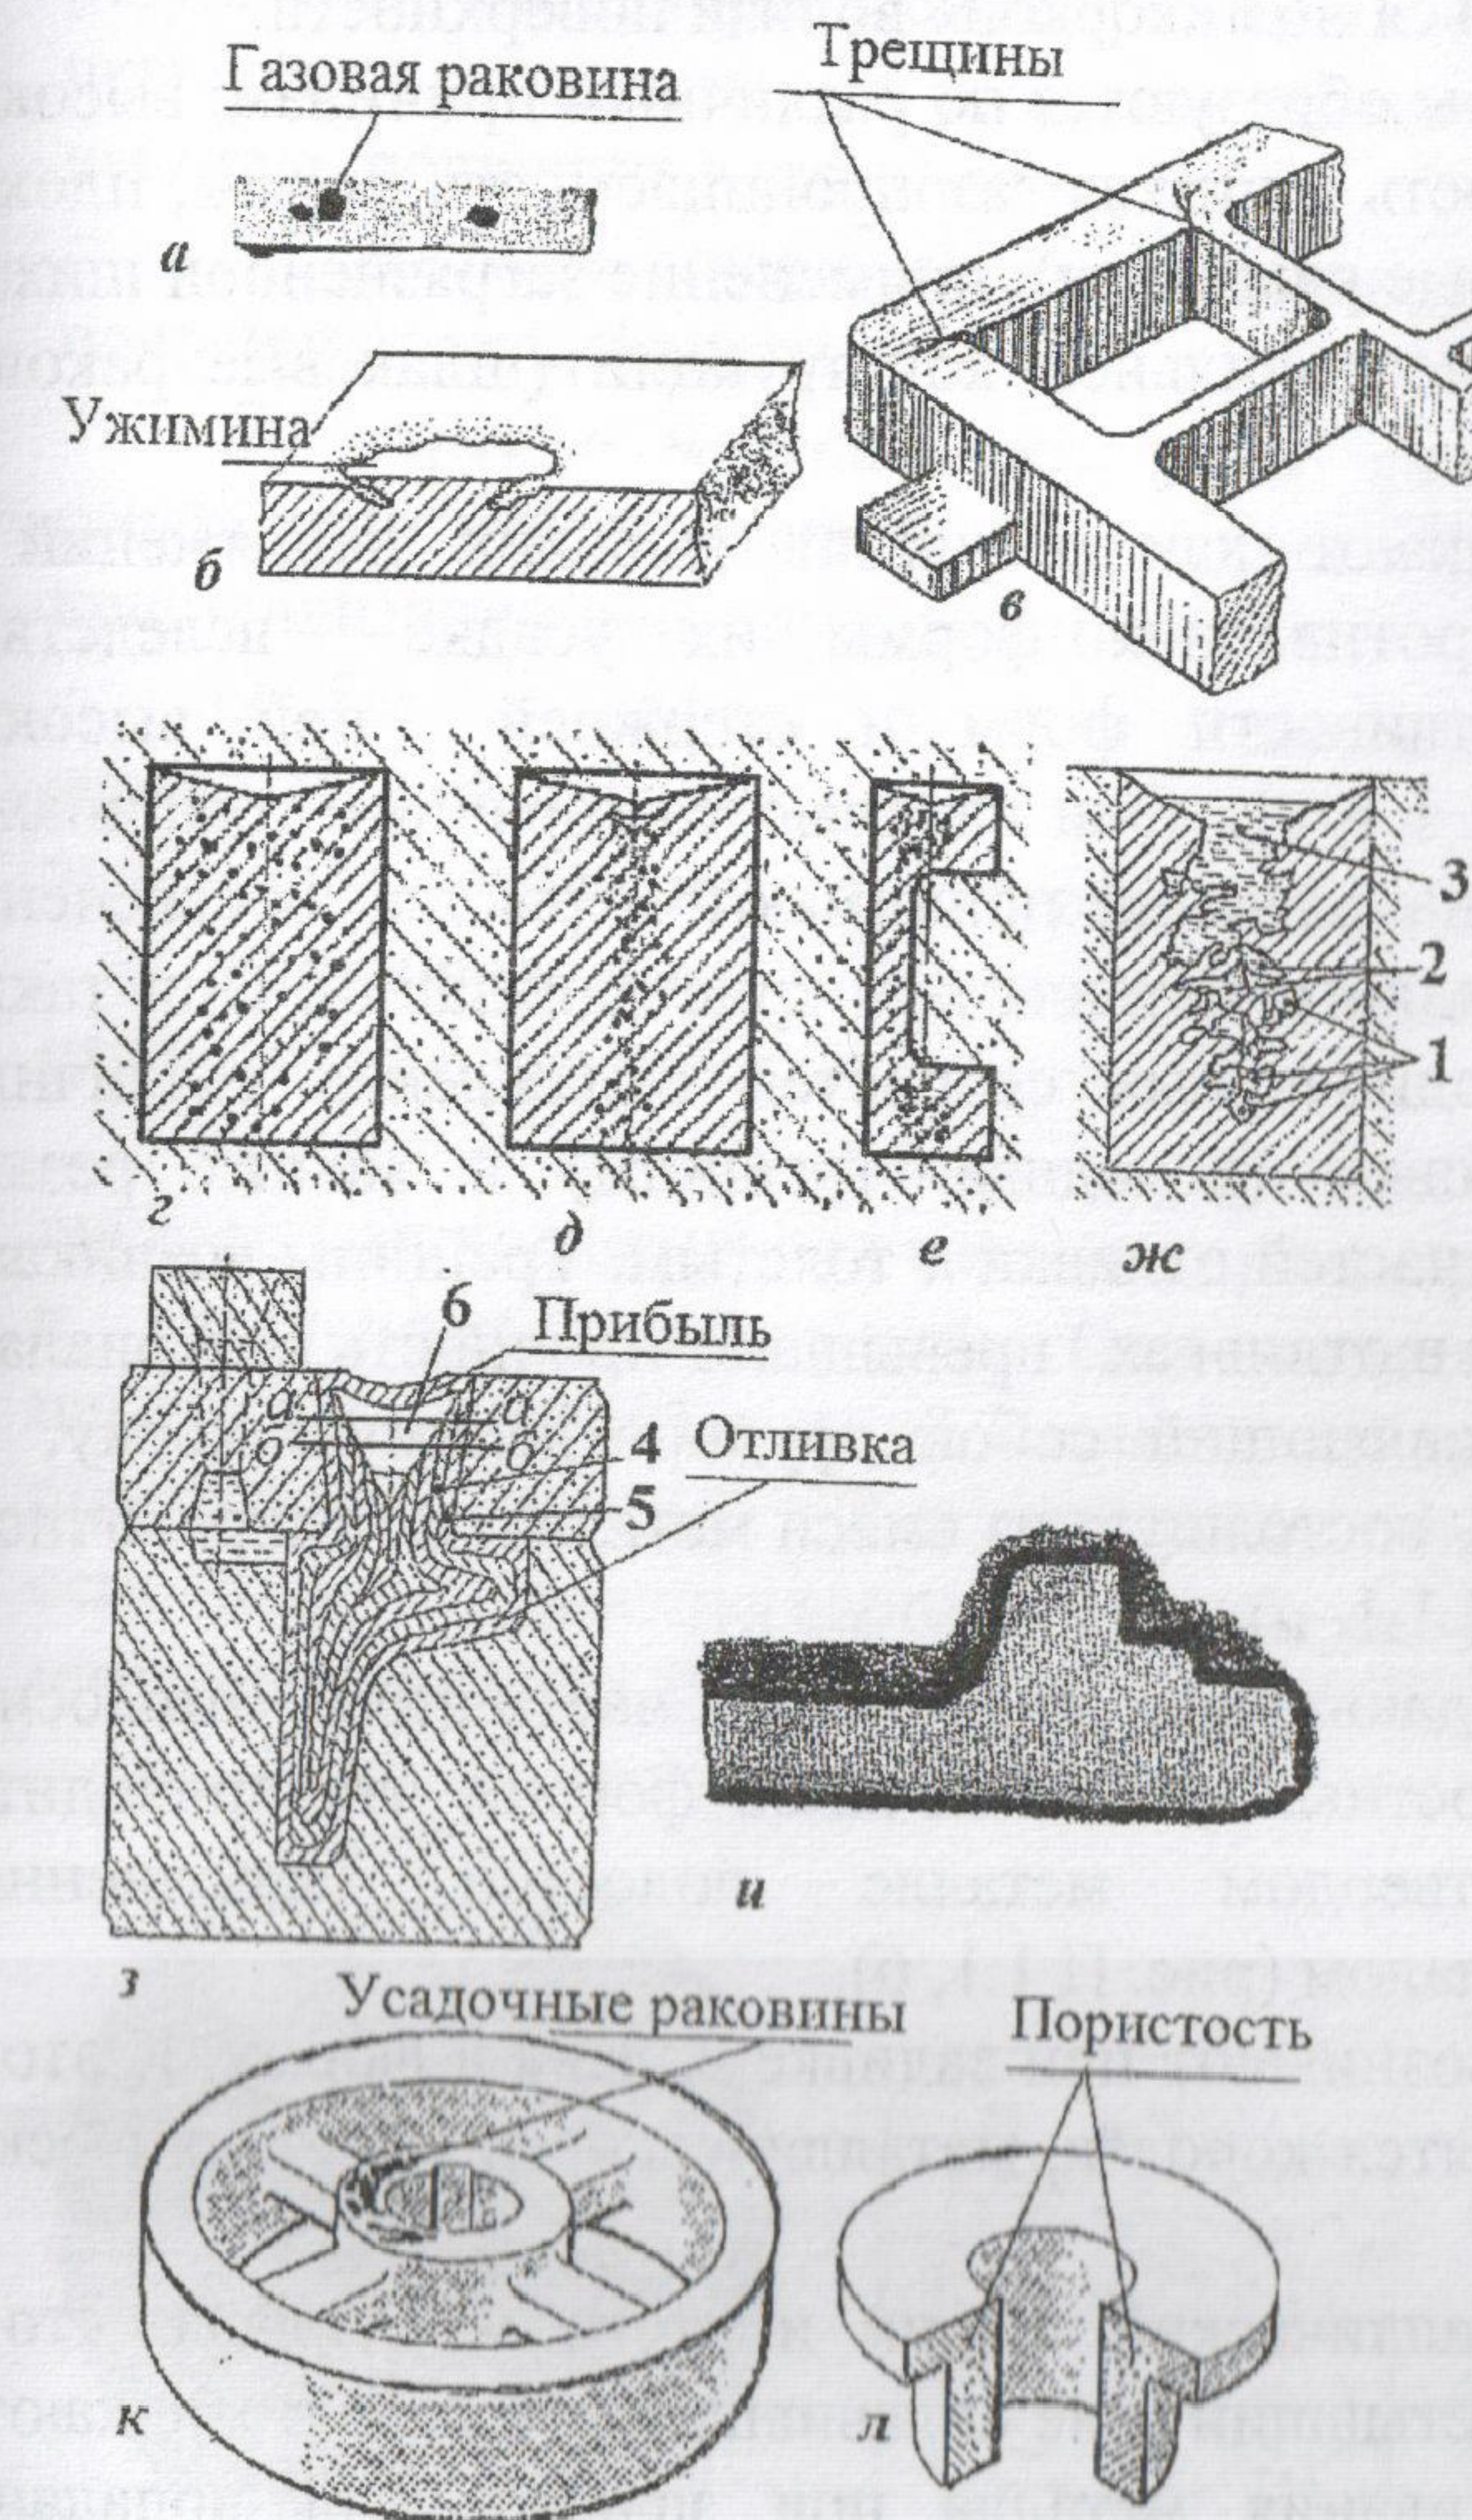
Некоторые характерные дефекты в отливках: а – газовая раковина; б – ужимины; в – трещины; г, д, е, ж – усадочная пористость; з – газовая раковина; и – пригар; к – усадочная раковина; л – пористость
